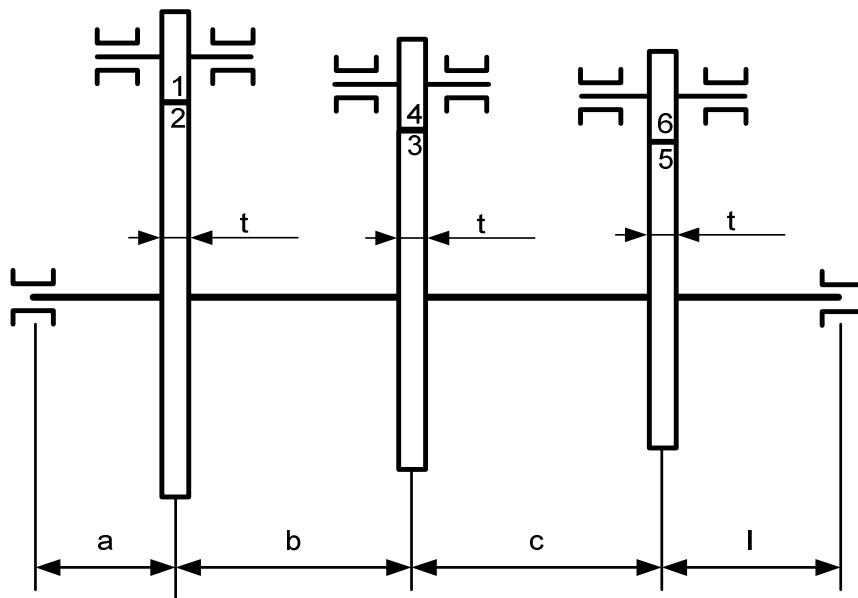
Кинематическая схема вала редуктора (развертка); $t=30\text{мм}$
